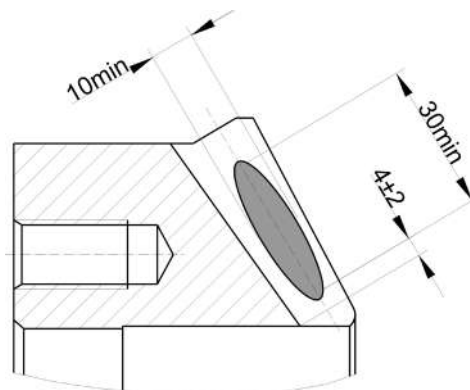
Расположение пятна контакта на ведомой шестерне редуктора
